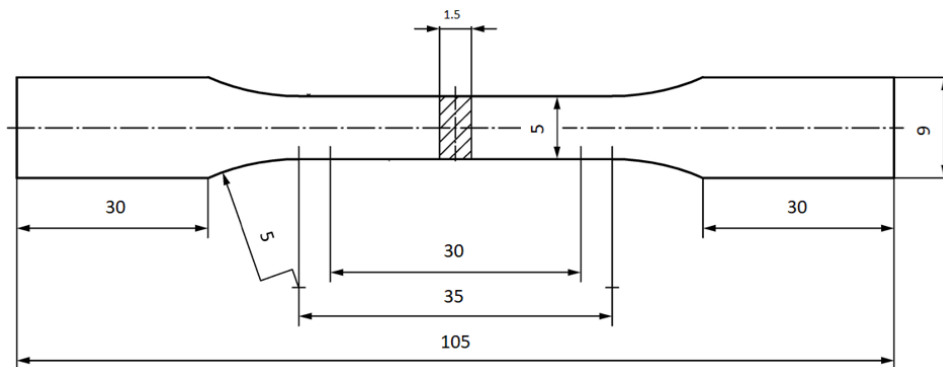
Technische Zeichnung der Flachzugprobengeometrie gemäß DIN EN ISO 6892-1
